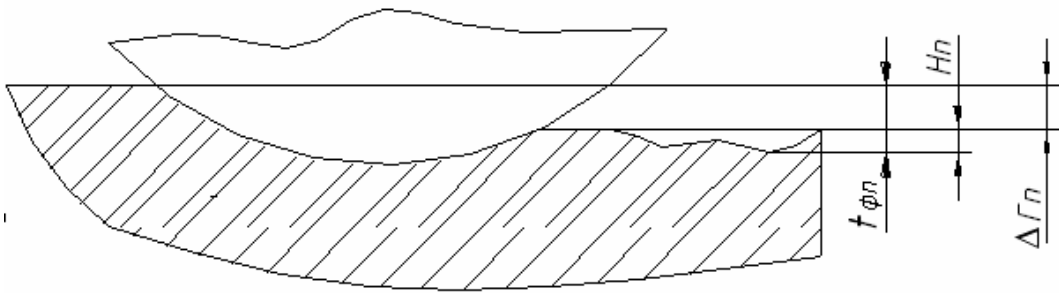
Схема взаємодії інструмента і заготовки при обробці деталей на основі металів і їх сплавів
